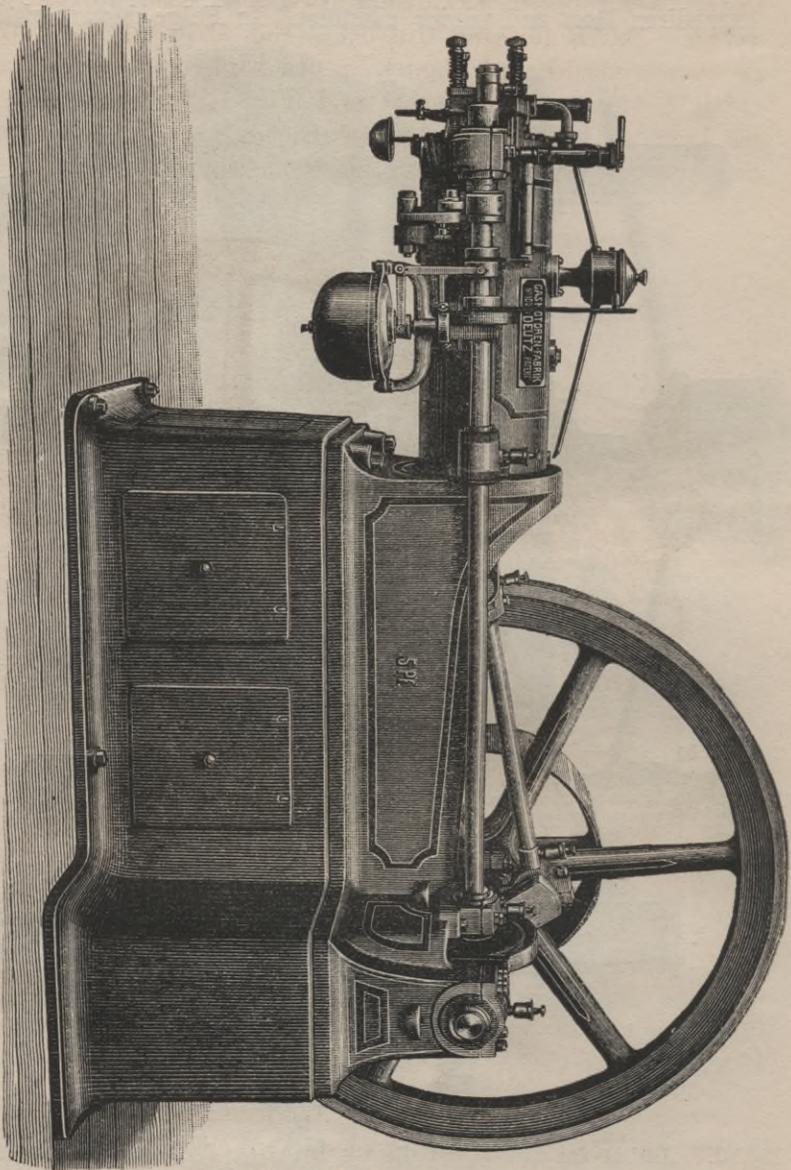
Ansicht der Steuerungstheile mit Regulator des Otto'schen Gasmotors.
